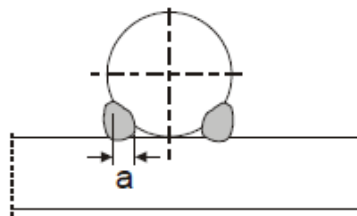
Espessura efectiva de um cordão de soldadura de um contorno de um varão [15]
